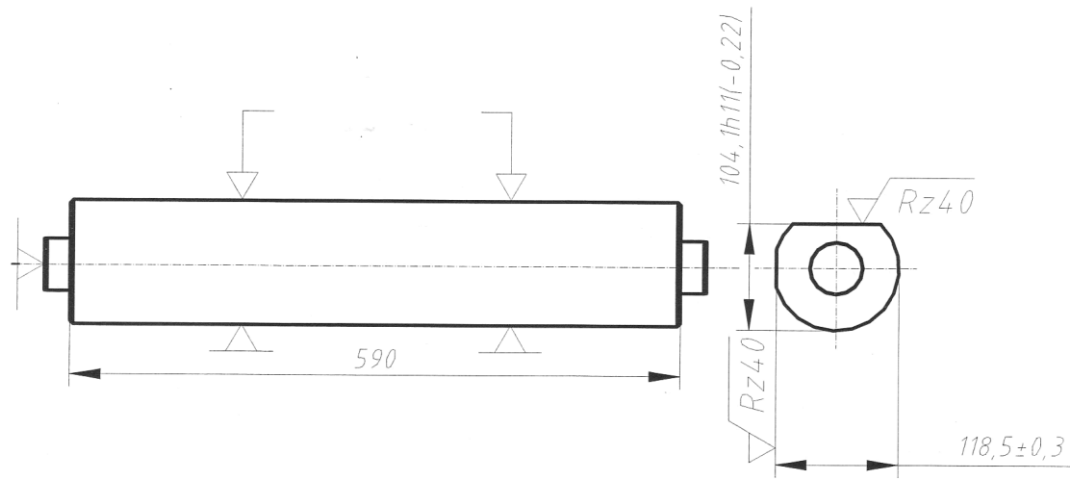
Ескіз обробки деталі операція №040
